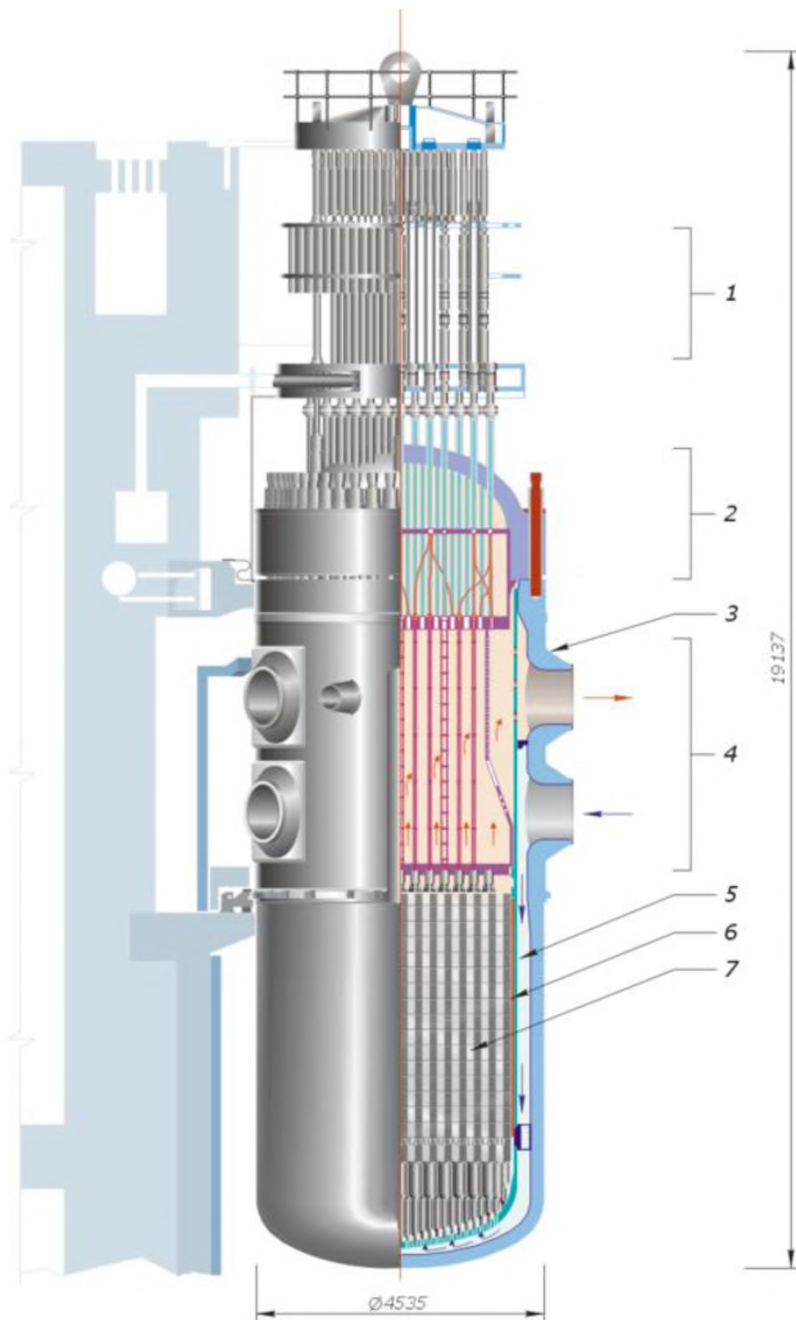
Реактор ВВЭР 1000: 1 — привод СУЗ; 2 — крышка реактора; 3 — корпус реактора; 4 — блок защитных труб (БЗТ); 5 — шахта; 6 — выгородка активной зоны; 7 — топливные сборки (ТВС) и регулирующие стержни;
